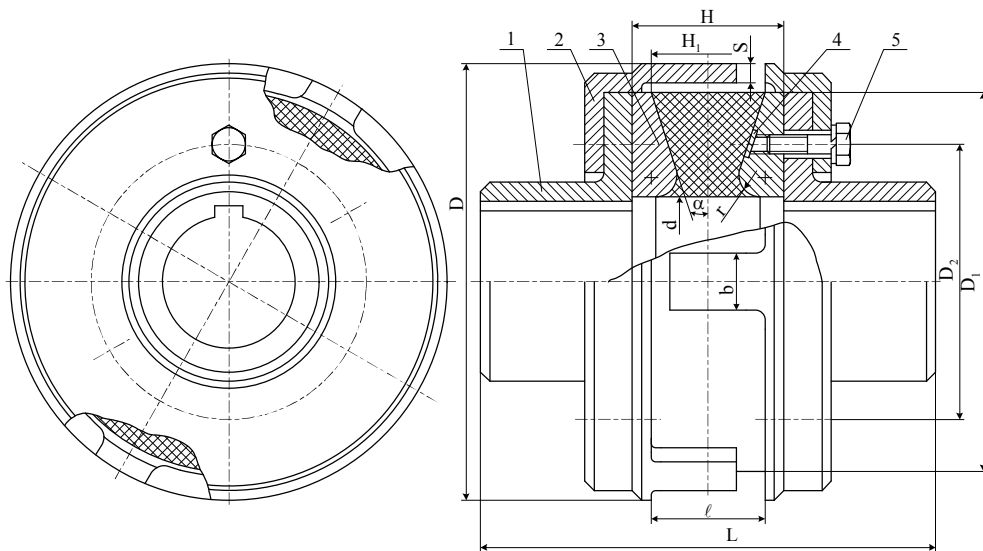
Конструкція муфти з привулканізованою гумовою шайбою
